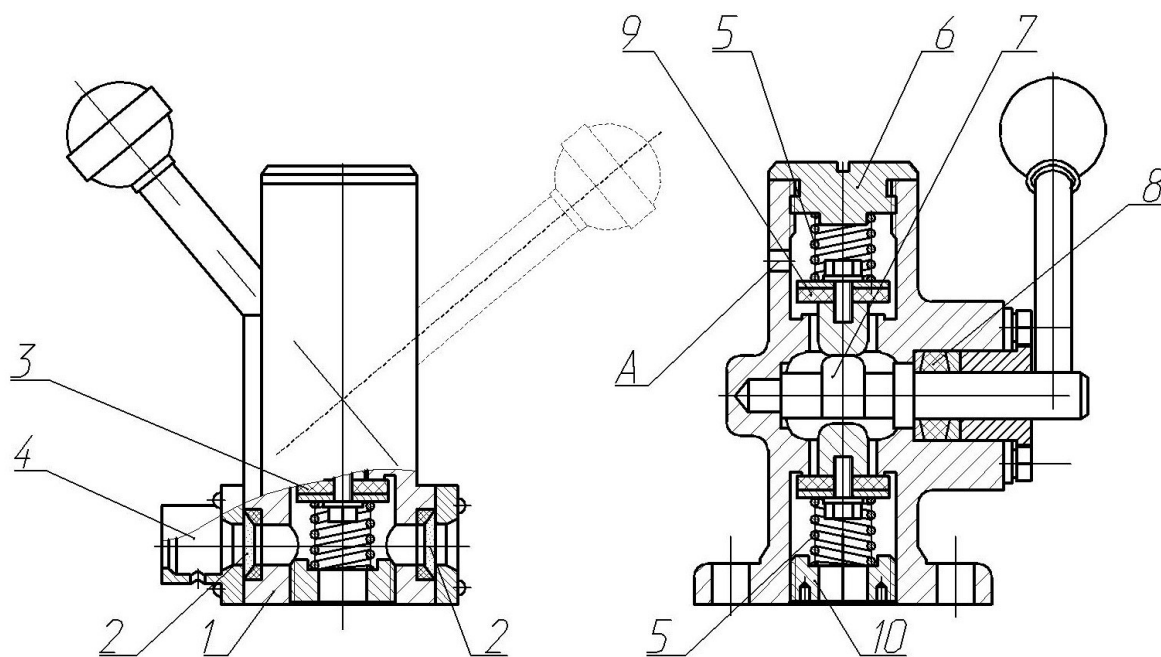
Вакуумный затвор: 1 – корпус; 2 – глазок; 3 – клапан нижний; 4-корпус патрона электрической лампы; 5- пружина; 6-гайка; 7- кулачковый валик с рукояткой; 8-сальниковое уплотнение; 9 – верхний клапан; 10 – гайка; А – отверстие для сообщения с атмосферой.
